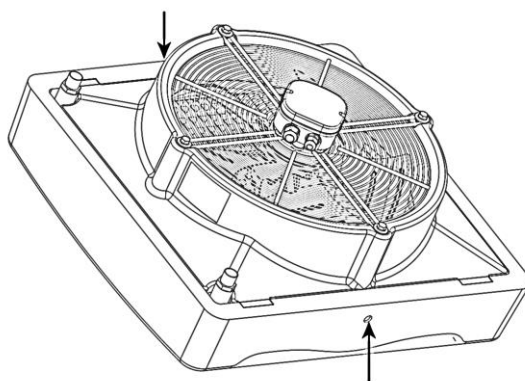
Места под отверстия для крепления кронштейна к корпусу R2
